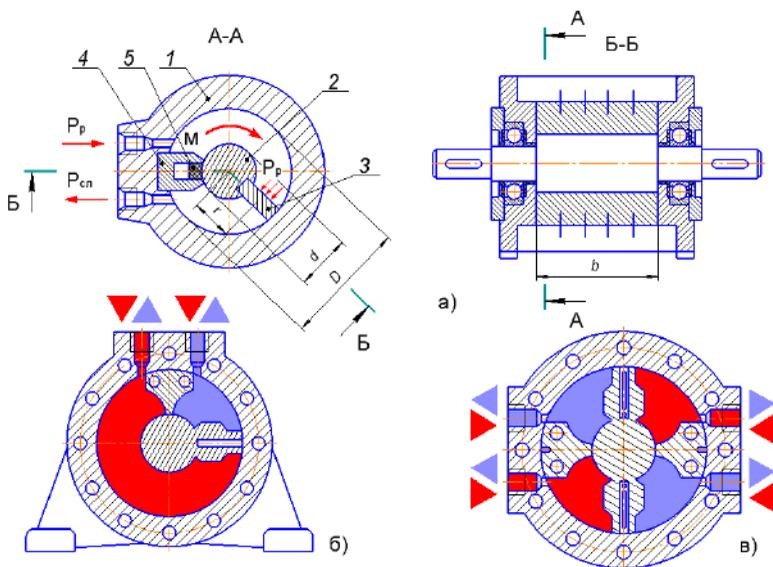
Лопатевий поворотний гідродвигун:
